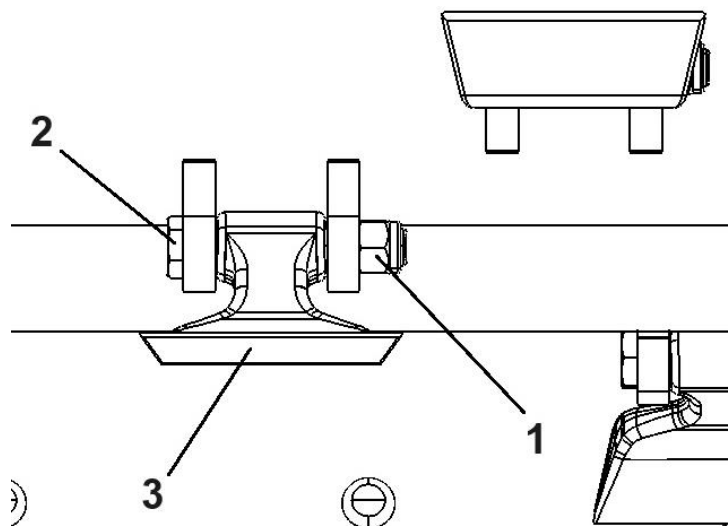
Austausch der Schlegelmesser: 1 – Befestigungsmutter, 2 – Befestigungsschraube, 3 – Schlegelmesser
